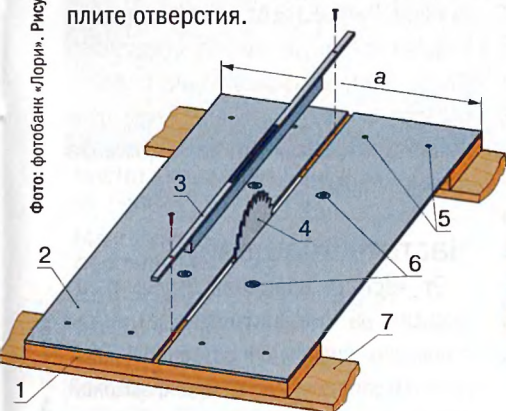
Стол распиловочного станка: 1 — фанерная перемычка; 2 — стальная пластина; 3 — вкладыш; 4 — пильный диск; 5 — шурупы; 6 — винты с головкой впотай; 7 — доска станины.
